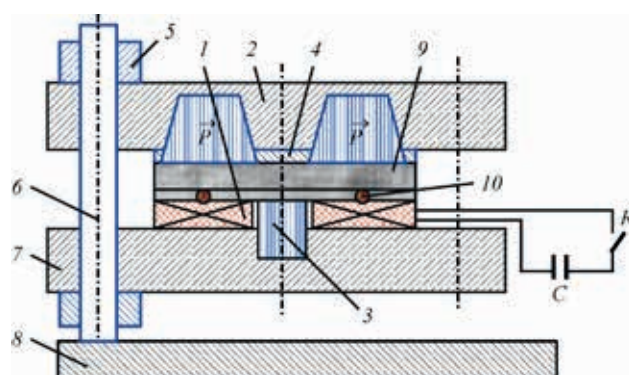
Конструктивна схема ОІЕМП металевих матеріалів: 1 – індуктор; 2 – верхня плита; 3 – вісь кріплення індуктора; 4 – зразок зварного з’єднання сплаву АМг6 $\delta = 1,0$ мм; 5 – гайка притискання; 6 – шпилька; 7 – нижня плита; 8 – базова опора; 9 – струмопровідний екран (рис. 1, в); 10 – зразок-імітатор зварного з’єднання; P – епюра розподілу електродинамічної сили по поверхні зразка; С – джерело ІЕМП; К – ключ запуску розрядного циклу
